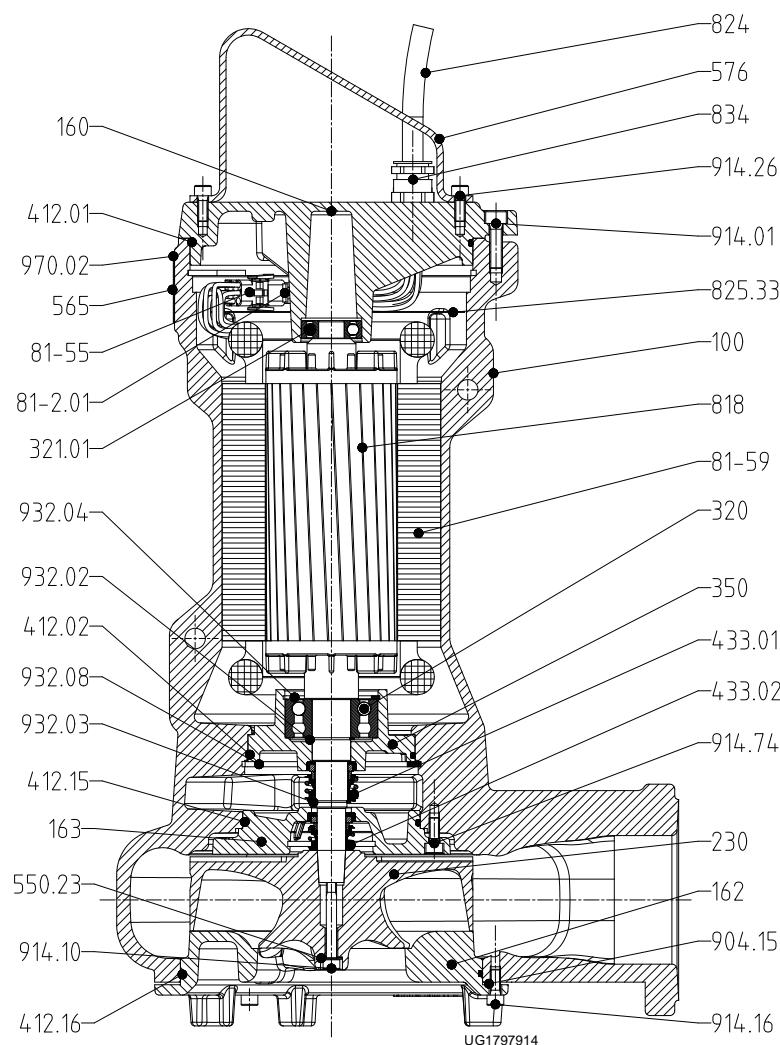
Сборочный чертеж для исполнения US, с рабочим колесом D-max
